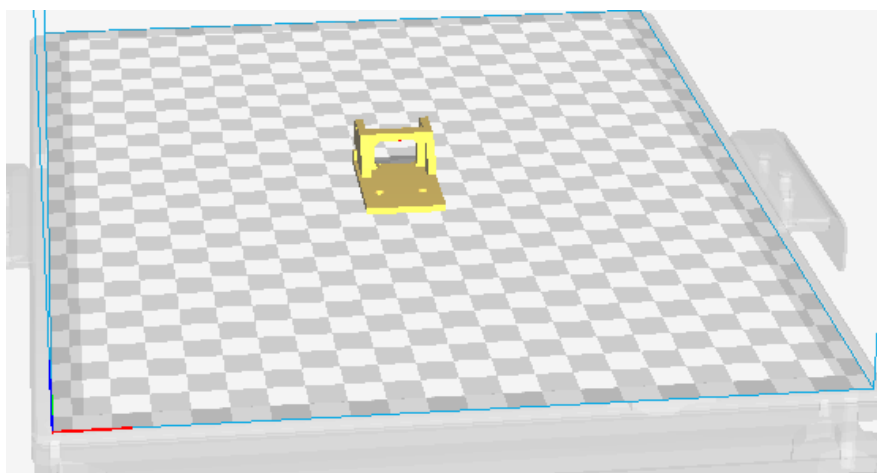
Posición de impresión extremo final de cadena portacable 2.
